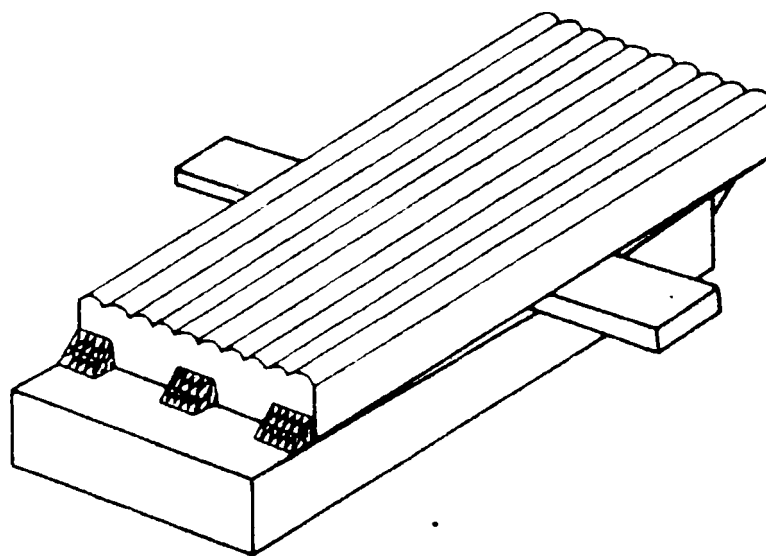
Încărcarea pe o suprafață pretensionată
